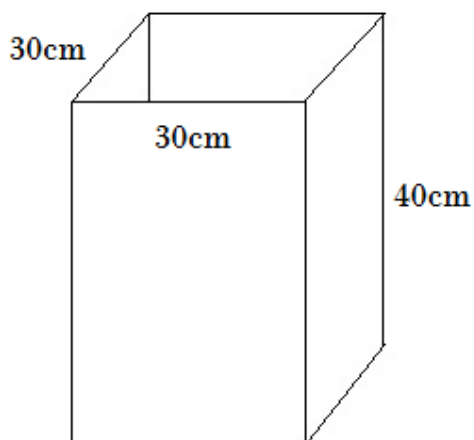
Vista Frontal Diseño de Tanque de Mezclado
